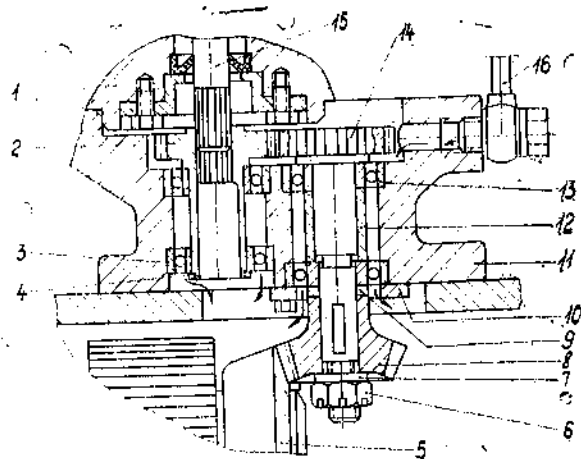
Привод регулятора скорости: 1—регулятор скорости; 2—ведомая шестерня; 3—шариковый подшипник; 4—пружинное кольцо; 5—шестерня распределительного вала; 6—корончатая гайка; 7—шайба; 8—приводная шестерня; 9—регулирующее кольцо; 10—кольцо; 11—корпус; 12—опорная втулка; 13—шариковый подшипник; 14—ведущая шестерня; 15—валик регулятора; 16—трубка для подвода смазки
